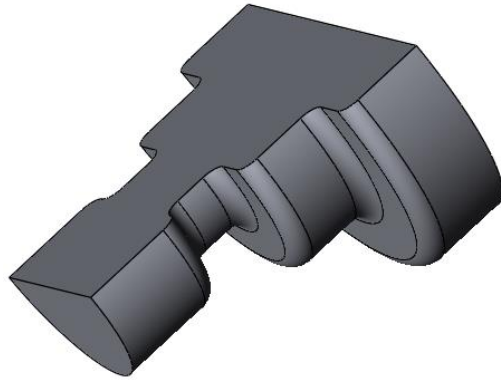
Imagen del CAD de la parte empleada como herramienta para la operación booleana de corte para el diseño del segundo tipo de soporte para la pieza 7.
